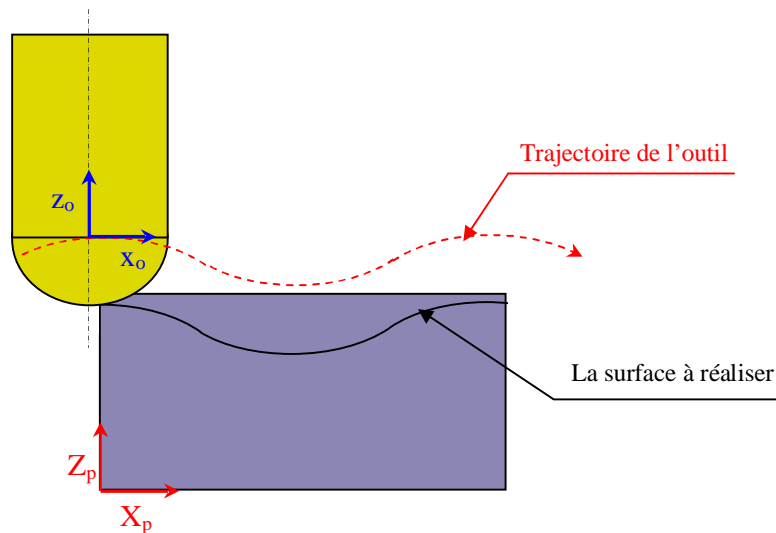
Géométrie de la pièce et positionnement de l'outil par rapport à la pièce.
